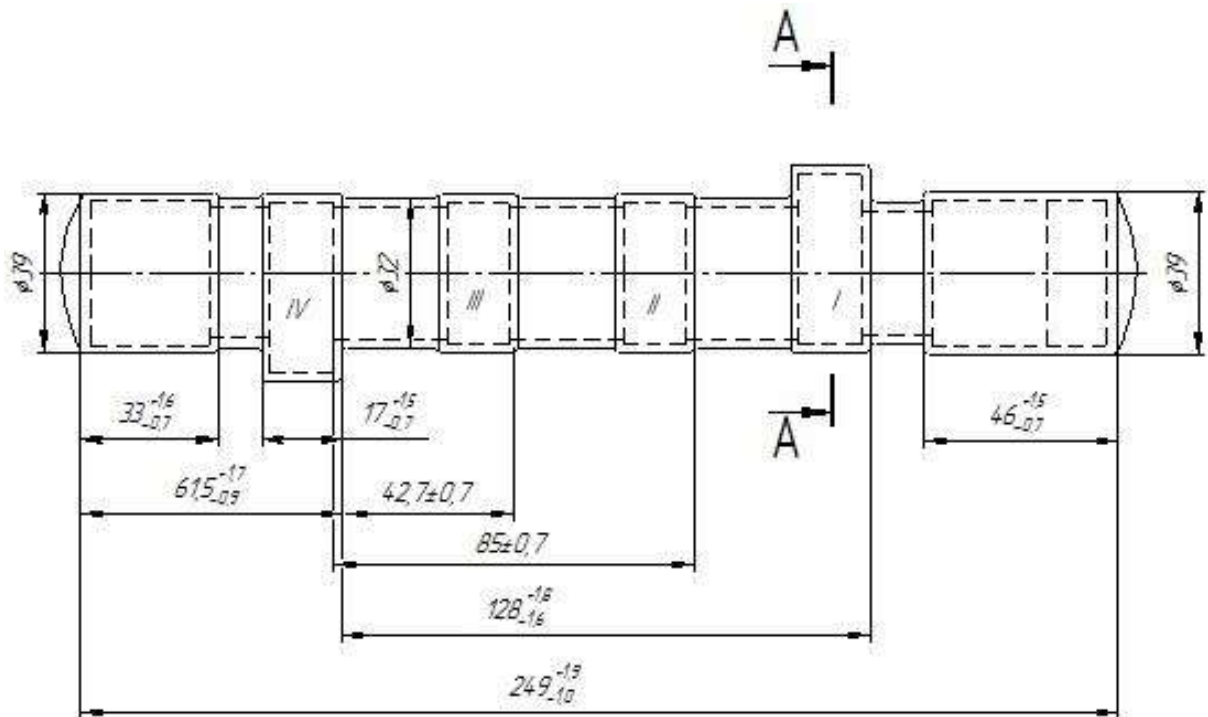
Эскиз заготовки вала кулачкового
